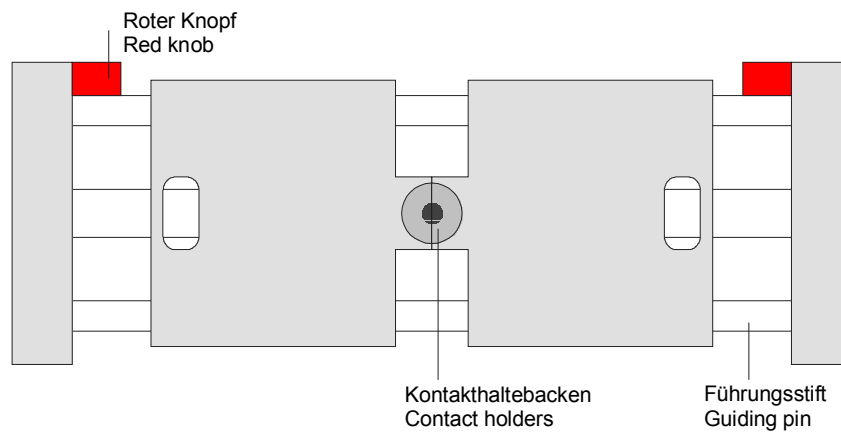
Kontakthalteinheit / Contact holding unit
